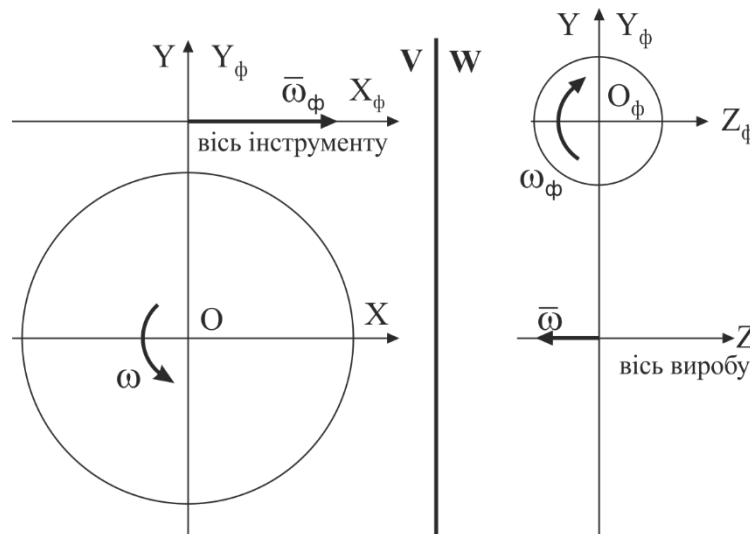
Схема обробки багатозубих виробів на зубофрезерному верстаті
